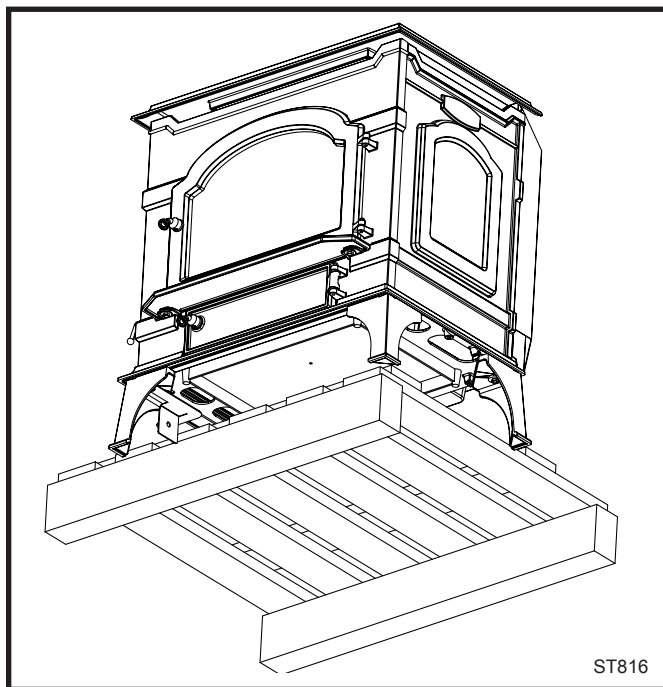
Tournez le poêle de façon à pouvoir installer une patte arrière.
